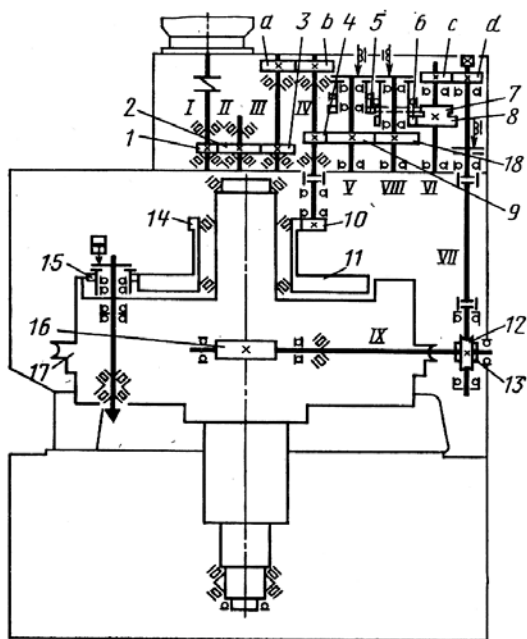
Кинематическая схема станка мод. КА-350
